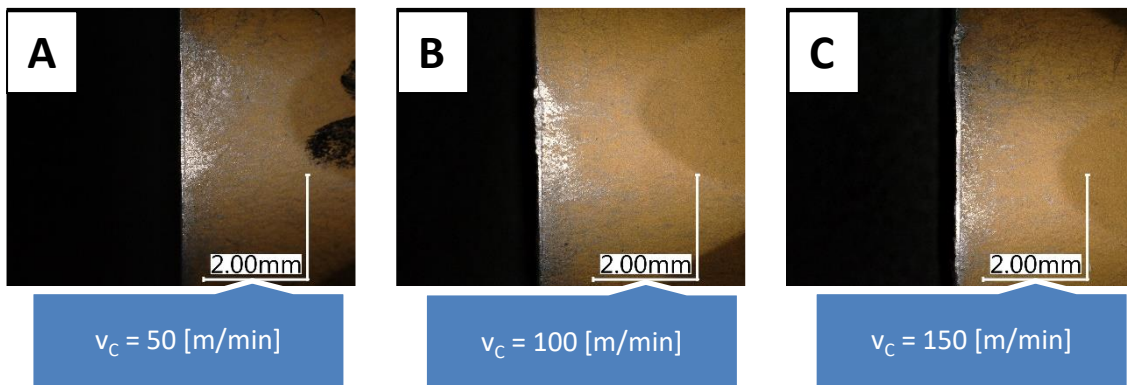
Hodnocení třísky RCKT-1204 MO-PM 4020
